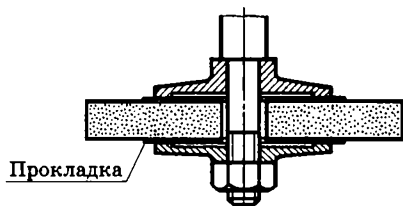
Установка шлифовального круга на шпинделе станка
